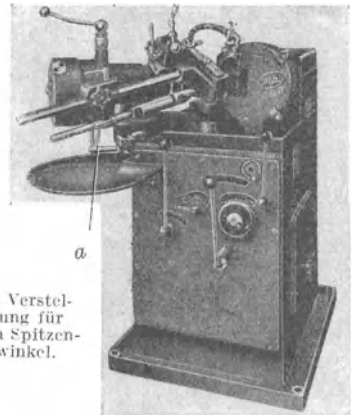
Spiralbohrer-Spitzenschleifmaschine.
